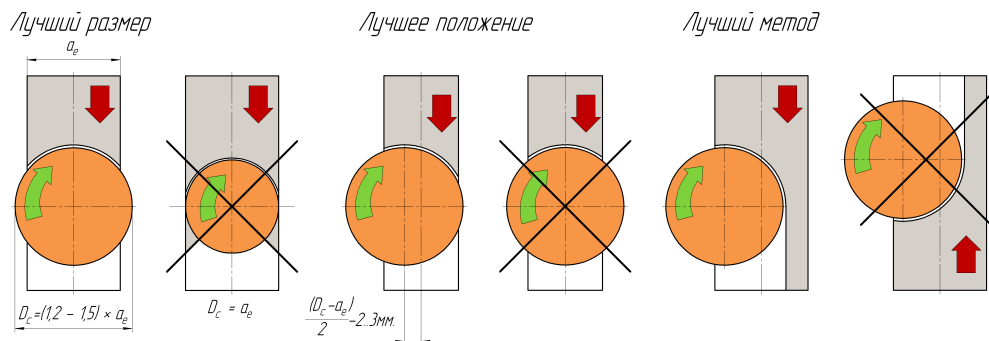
Варианты расположения фрезы относительно заготовки
